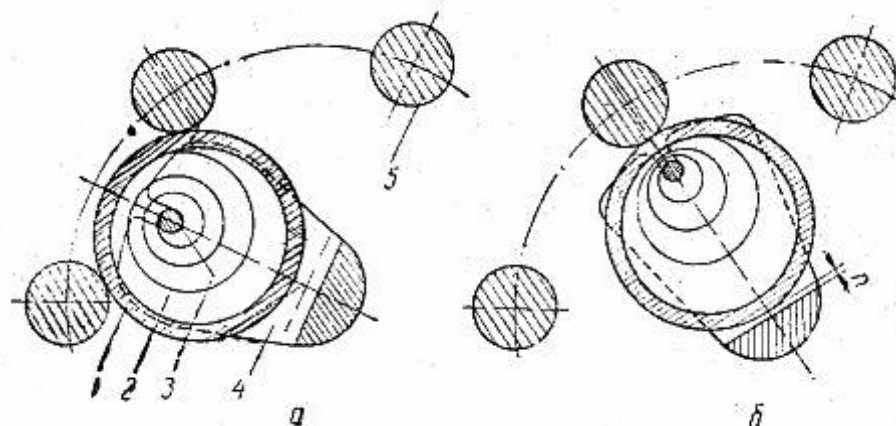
Кольцевой контакт: а - рабочее положение, б - промежуточное положение, 1 - контактное кольцо, 2 - спиральная ленточная пружина, 3 - ось пружины, 4 - коленчатый вал, 5 - контактный стержень.
